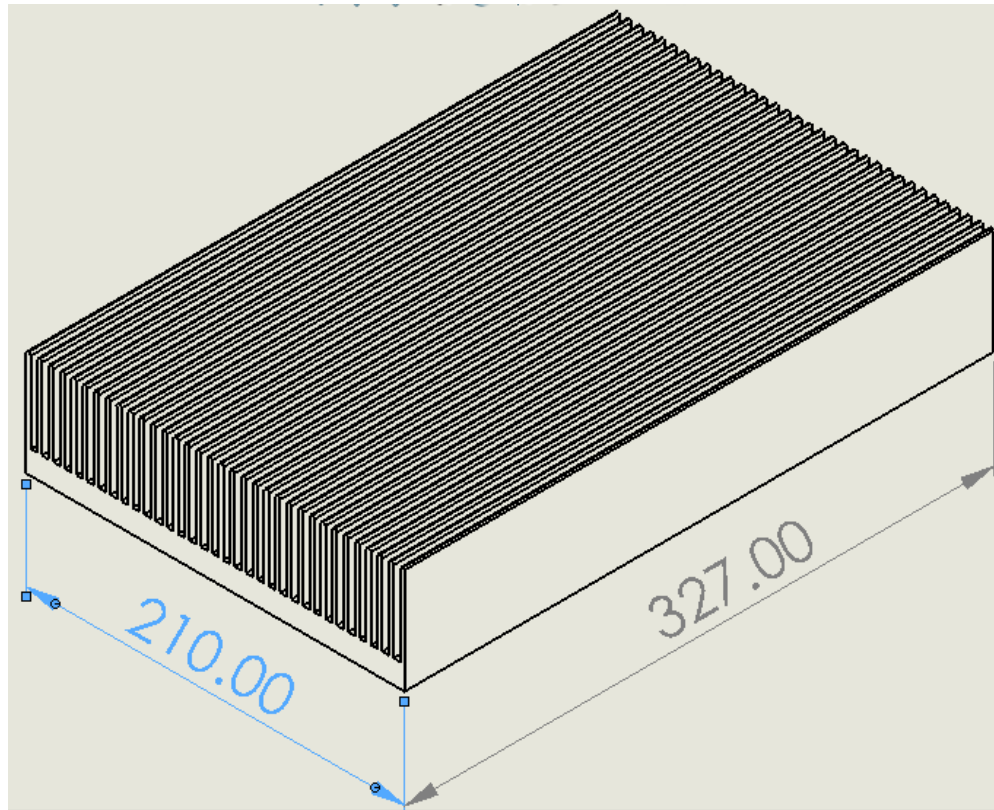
Dimensiones del Disipador de Aluminio para la cara Exterior Caliente del Módulo Peltier.
